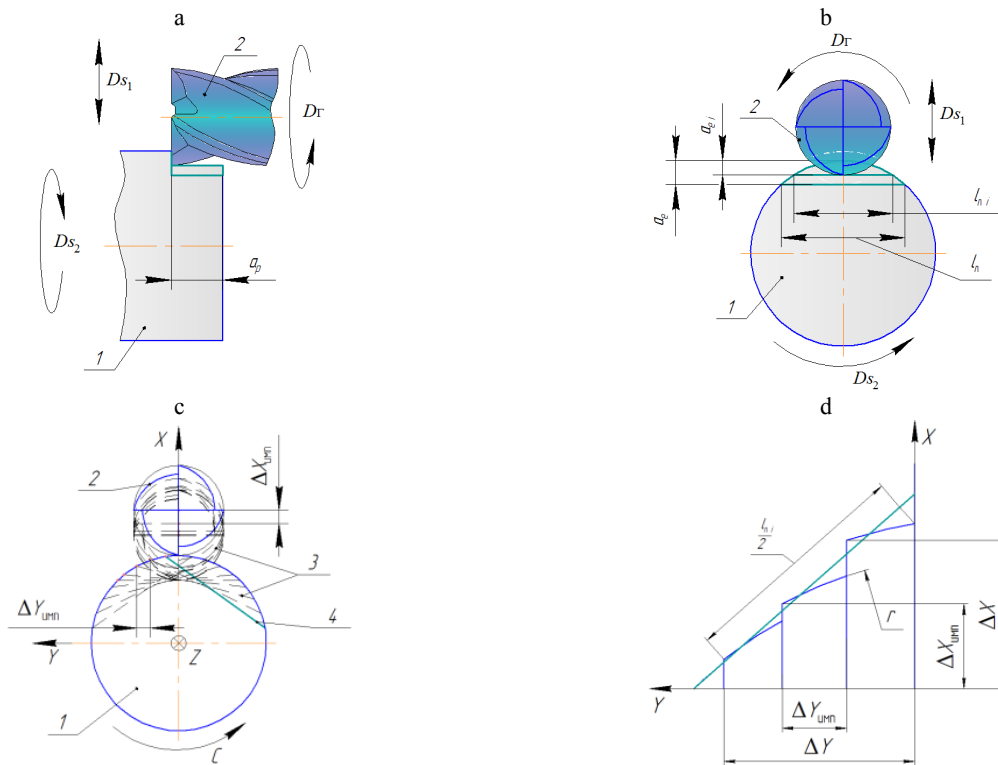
Схемы обработки (a, b) и формирования плоской поверхности (c) с реализацией линейной интерполяции (d) на токарном станке с ЧПУ модели EMCO S45: 1 – деталь; 2 – инструмент; 3 – промежуточные положения детали и инструмента; 4 – номинальная плоская поверхность
